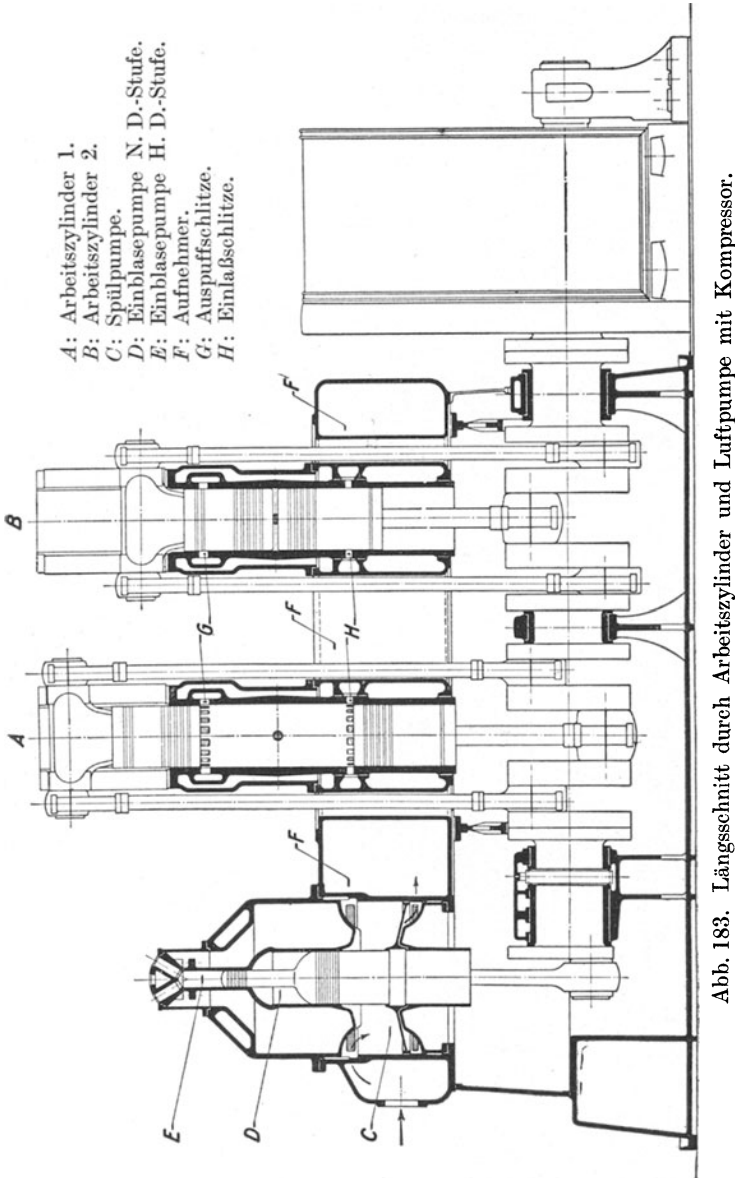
Längsschnitt durch Arbeitszylinder und Luftpumpe mit Kompressor.
